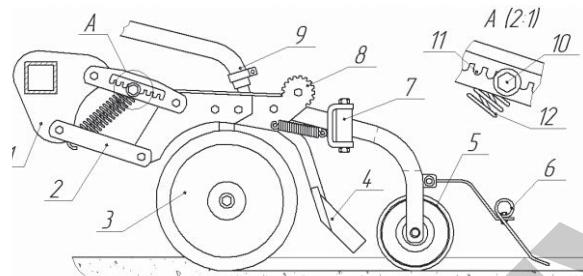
Комбинированный сошник для посева мелкосемянных культур: 1 – крепление; 2 – параллелограммный механизм; 3 – бороздкоформирующий каток; 4 – высеивающая система для семян; 5 – прикатывающее колесо; 6 – загортач; 7 – шарнир; 8 – храповой механизм; 9 – патрубок подачи семян; 10 – регулировочный болт; 11 – сектора; 12 – натяженная пружина
